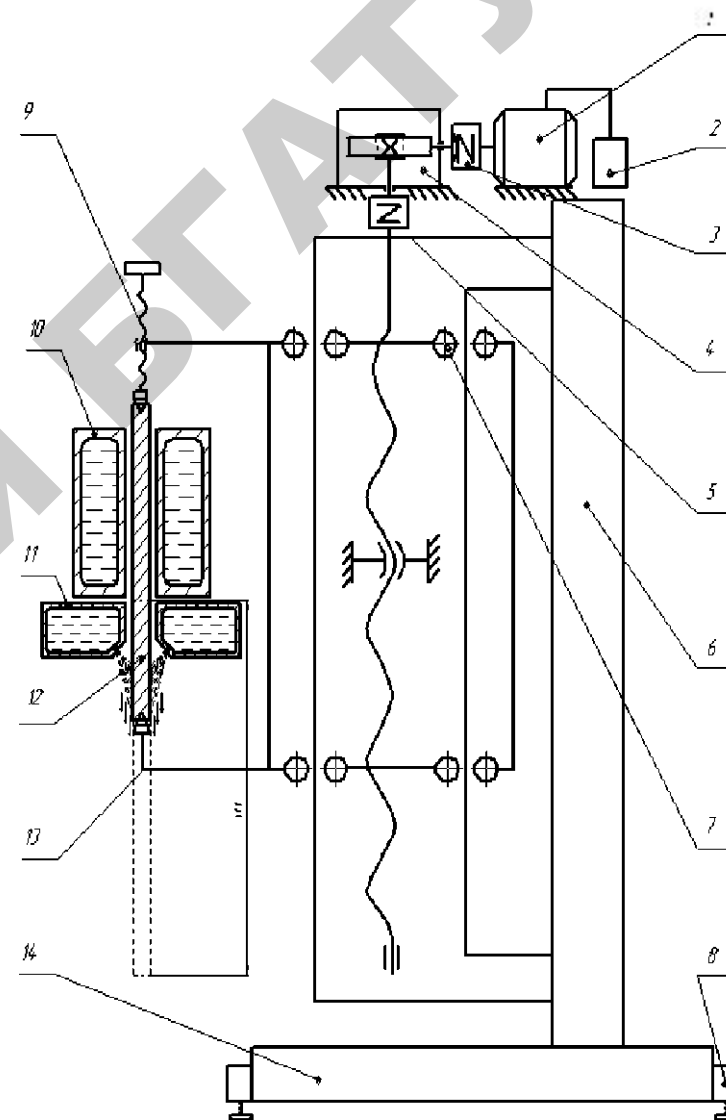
Кинематическая схема установки для вертикального перемещения заготовки:
